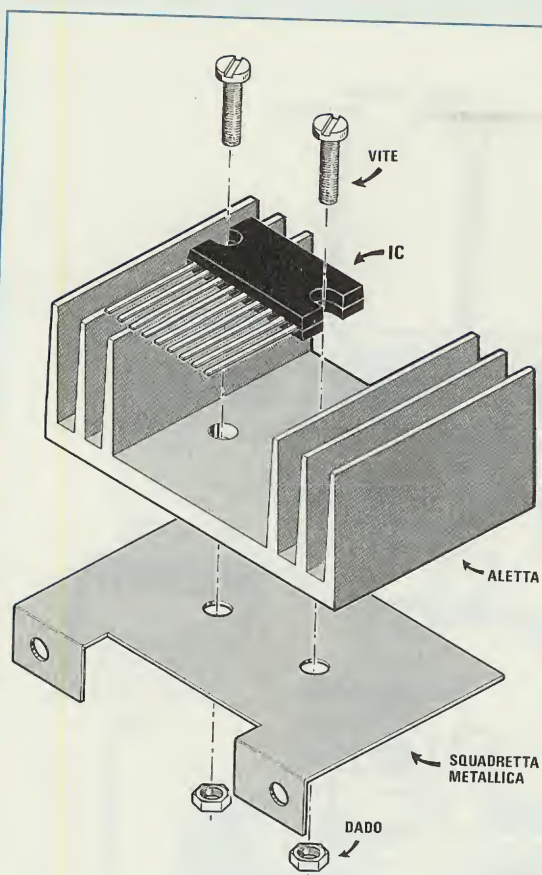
Nel kit, oltre all'aletta di raffreddamento troverete anche una squadretta metallica. Come potete vedere in questo disegno, l'integrato IC2 andrà applicato all'interno dell'aletta. Con le due viti che utilizzerete per fissare l'integrato, bloccherete anche la squadretta di fissaggio a L (fig.7).
